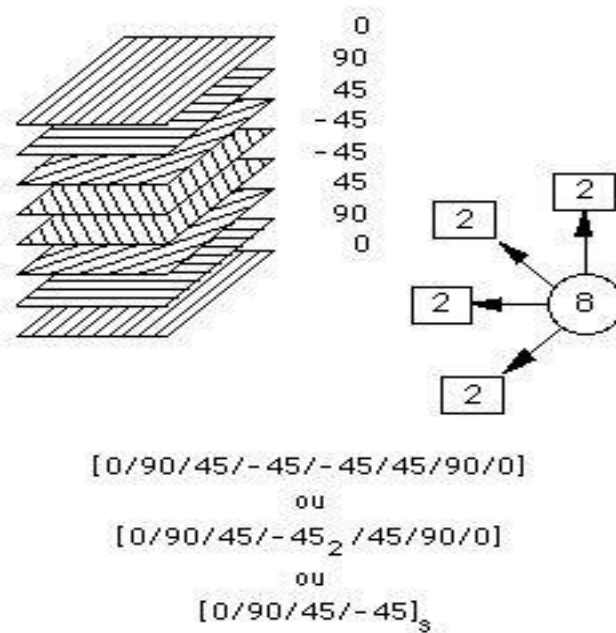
Exemple du plan du drapage d'un composite stratifié.
